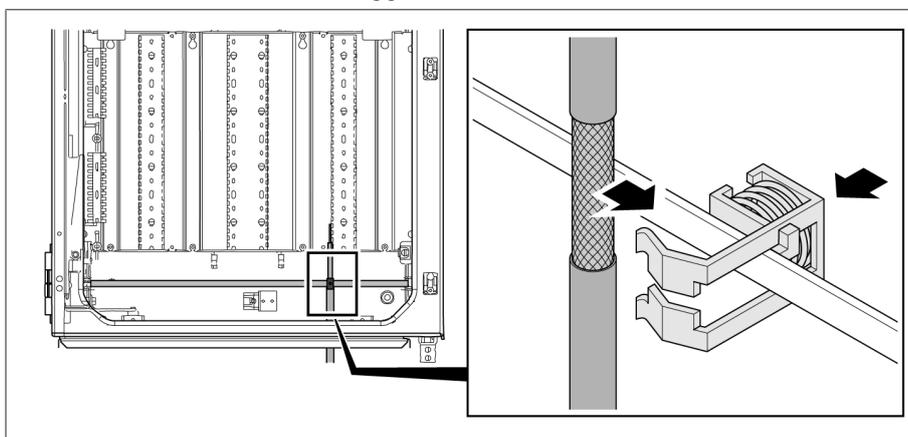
Applicazione della schermatura del cavo alla barra di messa a terra con staffa di bloccaggio
